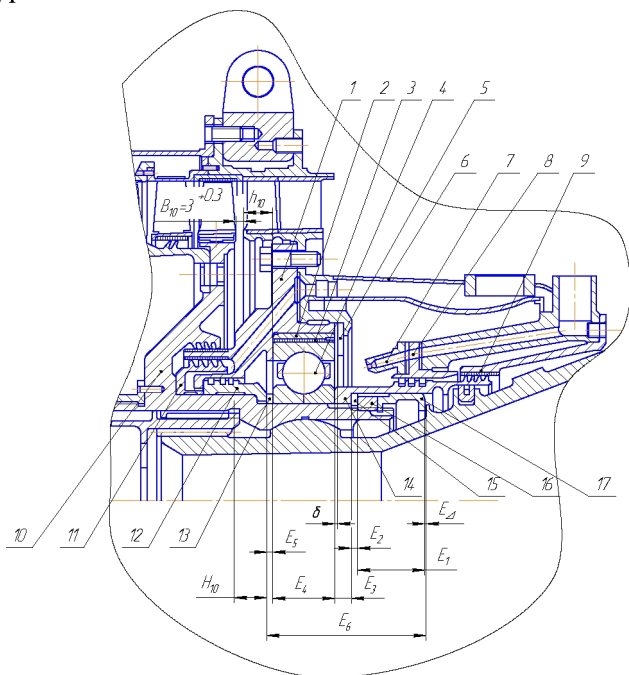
Задняя опора компрессора: 1 – корпус опоры, 2 – кольцо демпфера наружное; 3 – демпфер; 4 – шарикоподшипник, 5 – кольцо регулировочное, 6 – корпус лабиринтов, 7 – форсунка, 8 – втулка, 9 – втулка, 10 – диск десятой ступени, 11 – кольцо лабиринтное, 12 – кольцедержатель, 13 – кольцо регулировочное, 14 – кольцедержатель, 15 – кольцо регулировочное, 16 – гайка, 17 – втулка контровочная
